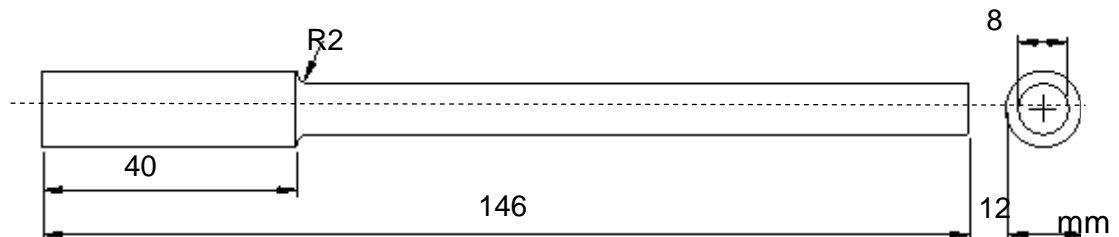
Dimensiones de las probetas para el ensayo en la máquina de fatiga a flexión rotativa.
